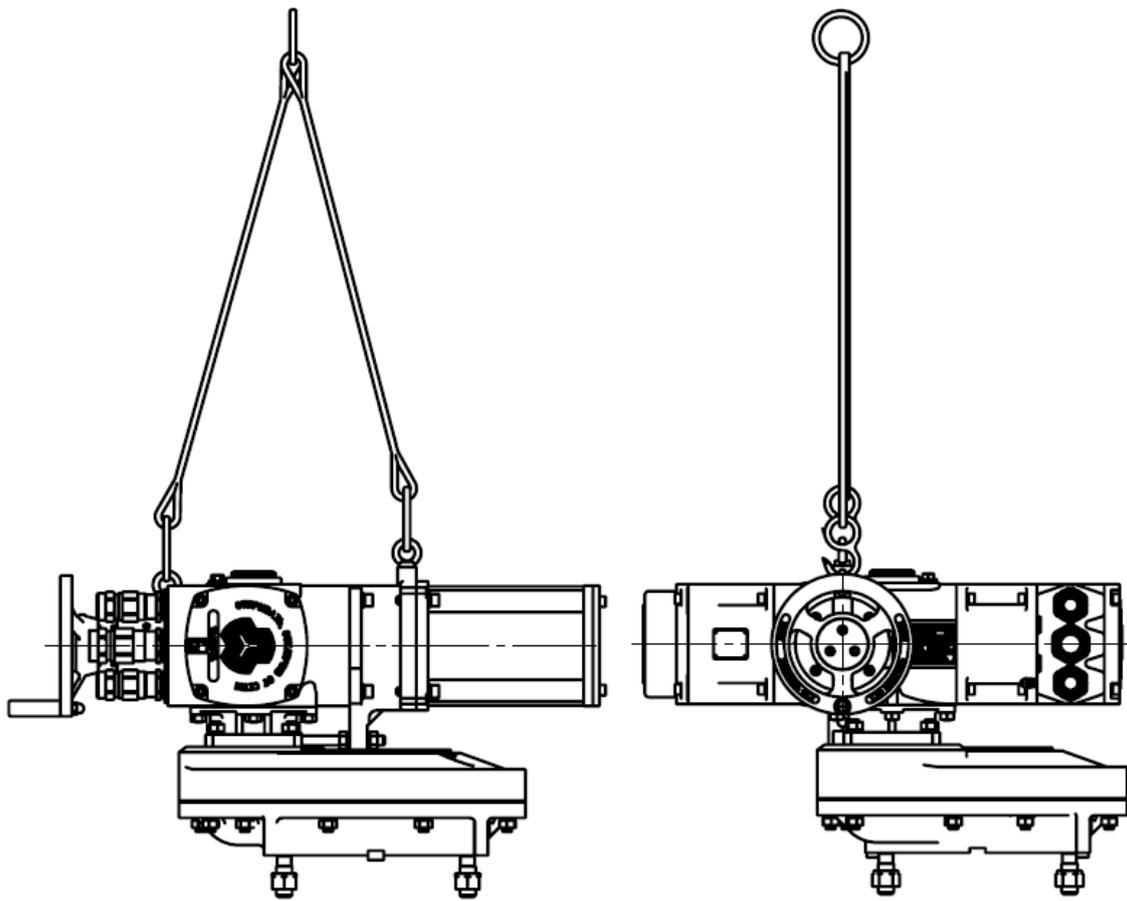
в – Схема строповки привода конструктивной схемы 410
